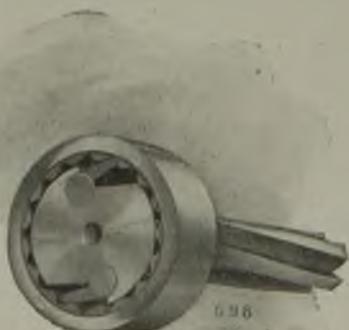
Umsetzvorrichtung der Ingersoll-Maschine.
